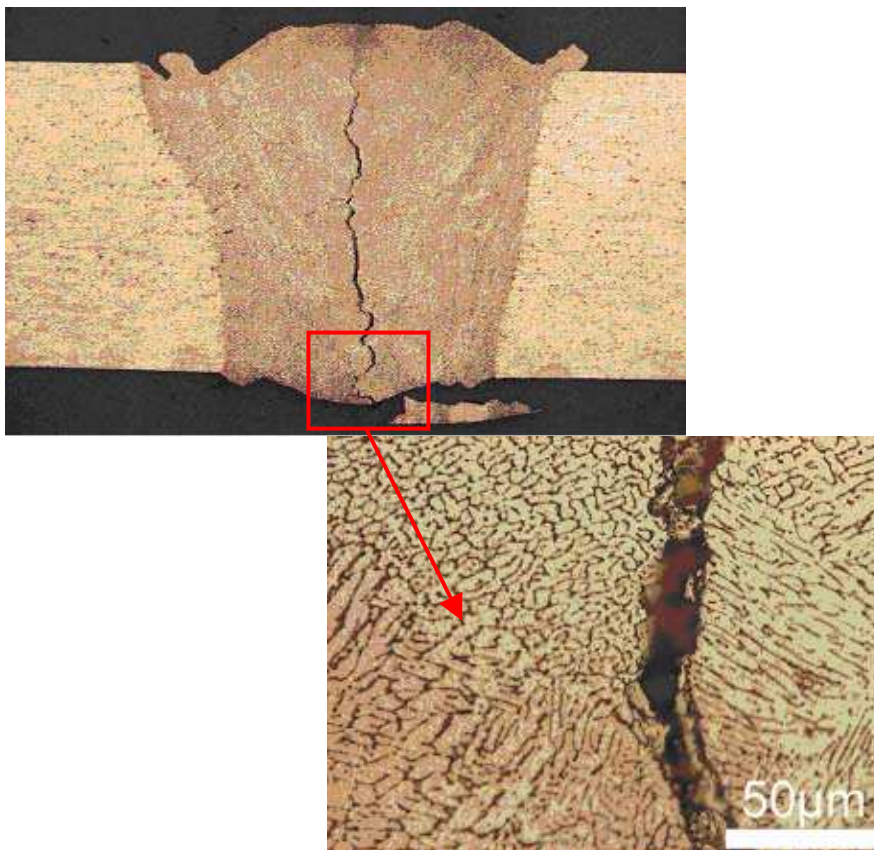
fissure à chaud dans une soudure bord à bord.
